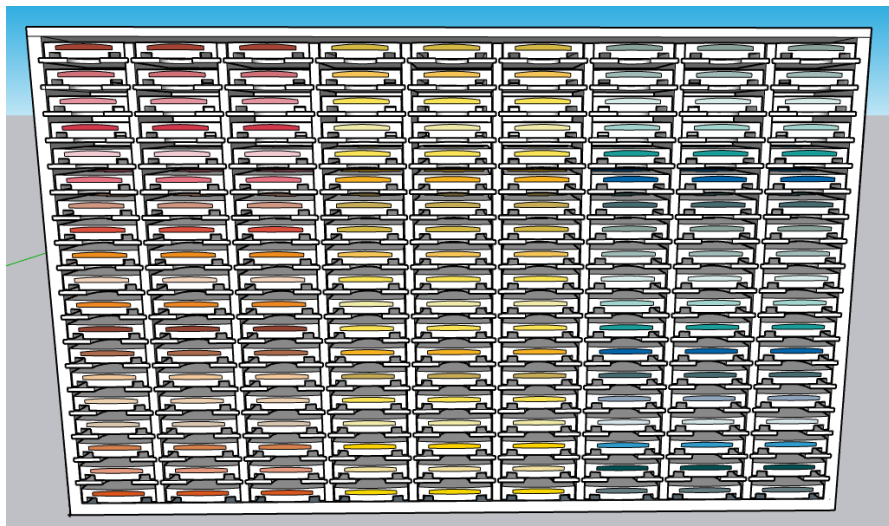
Desain Rak Penyimpanan Alternatif 1 (Drawing)
